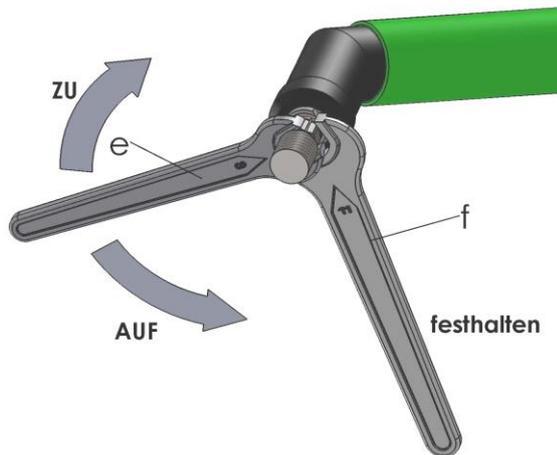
Werkzeugwechsel Spannzange ZG 4
